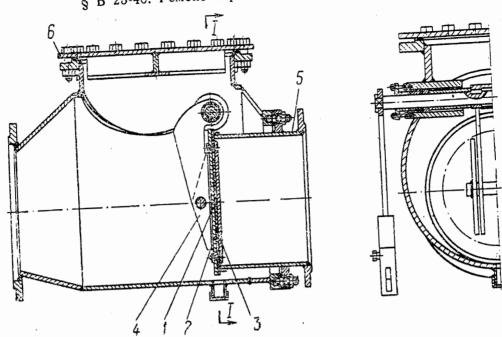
Обратный клапан. 1 — диск клапана; 2 — прокладка клапана; 3 — прижимной диск; 4 — ребро диска; 5 — входной патрубок; 6 — крышка.
